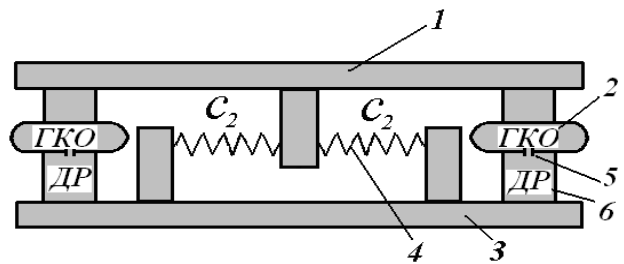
Схема конструкции второй ступени рессорного подвешивания с применением регулятора корректора жесткости: 1 – грузовая платформа, 2 – пружины второй ступени подвешивания, 3 – опорная платформа, 4 – пружины корректора жесткости, 5 – гайка регулировочная, 6 – винт регулировочный.
